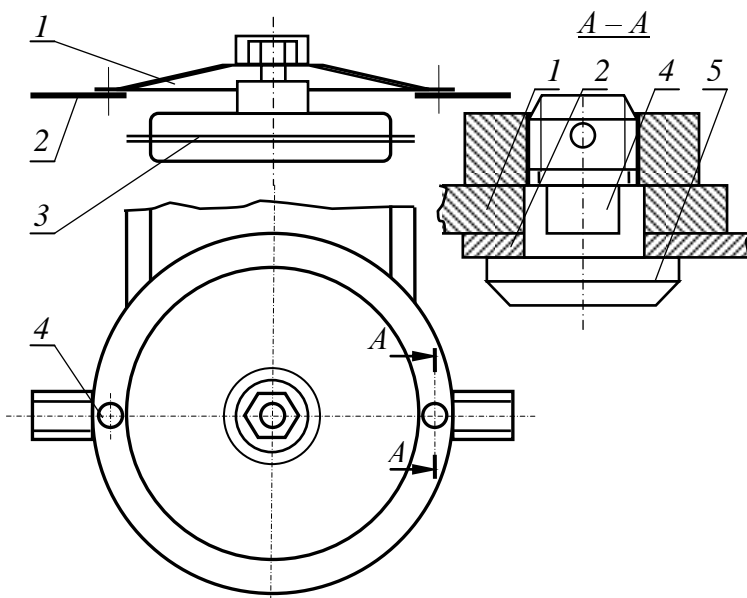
Схема ротора с шарнирно закрепленными на диске ножами.
